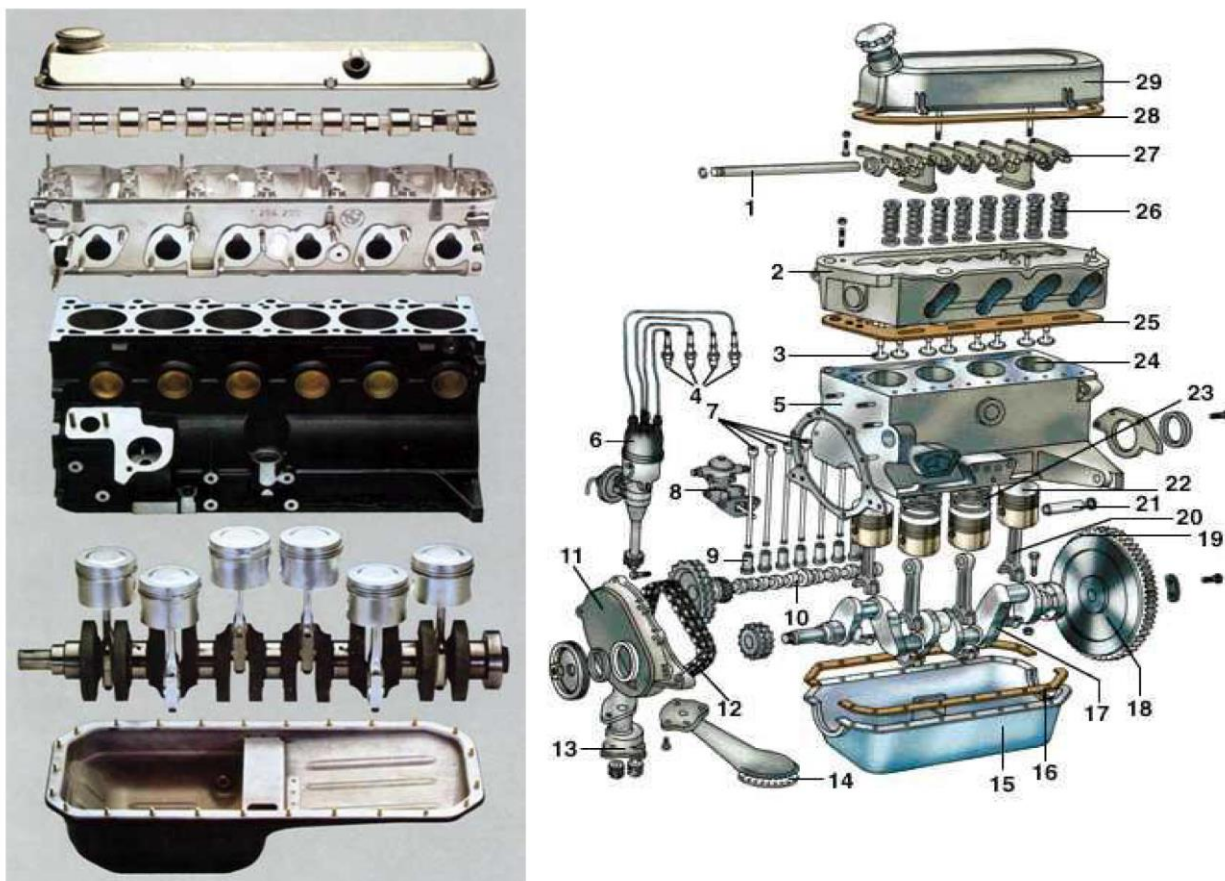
Vue éclatée d'un moteur à explosion [3]
